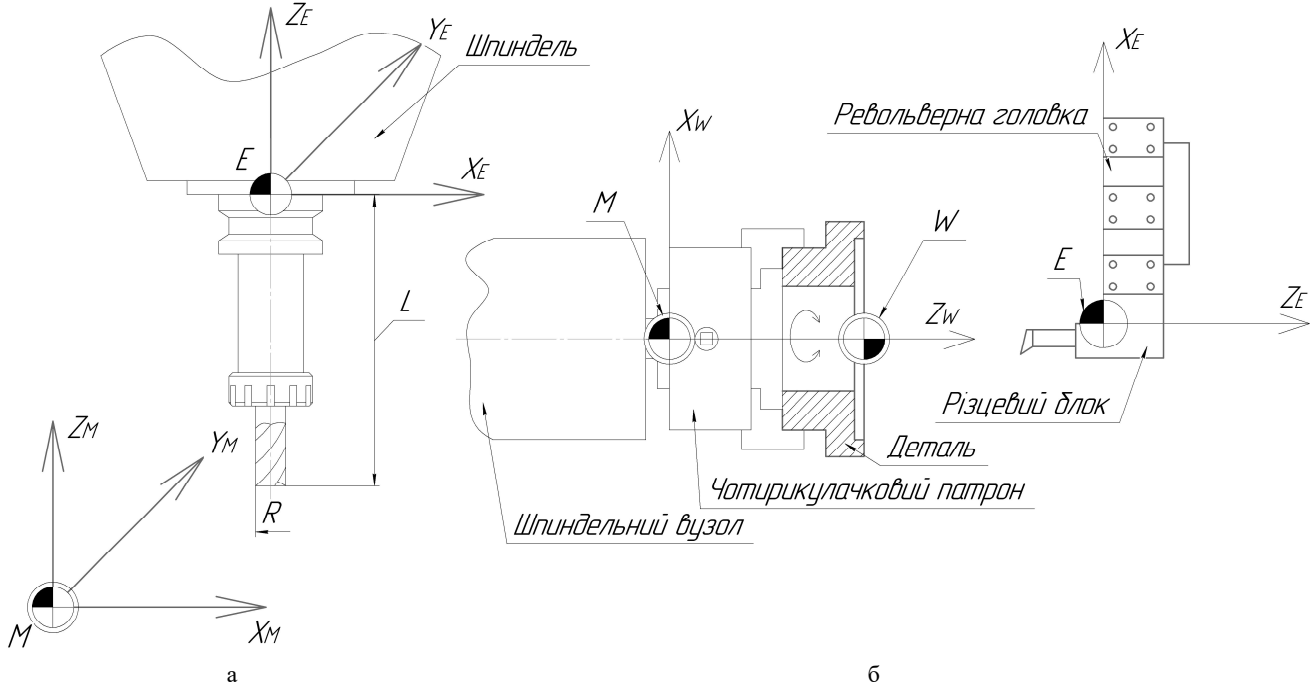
Розташування нульової точки інструменту (E) на фрезерних(а) і токарних верстатах з ЧПК(б)
